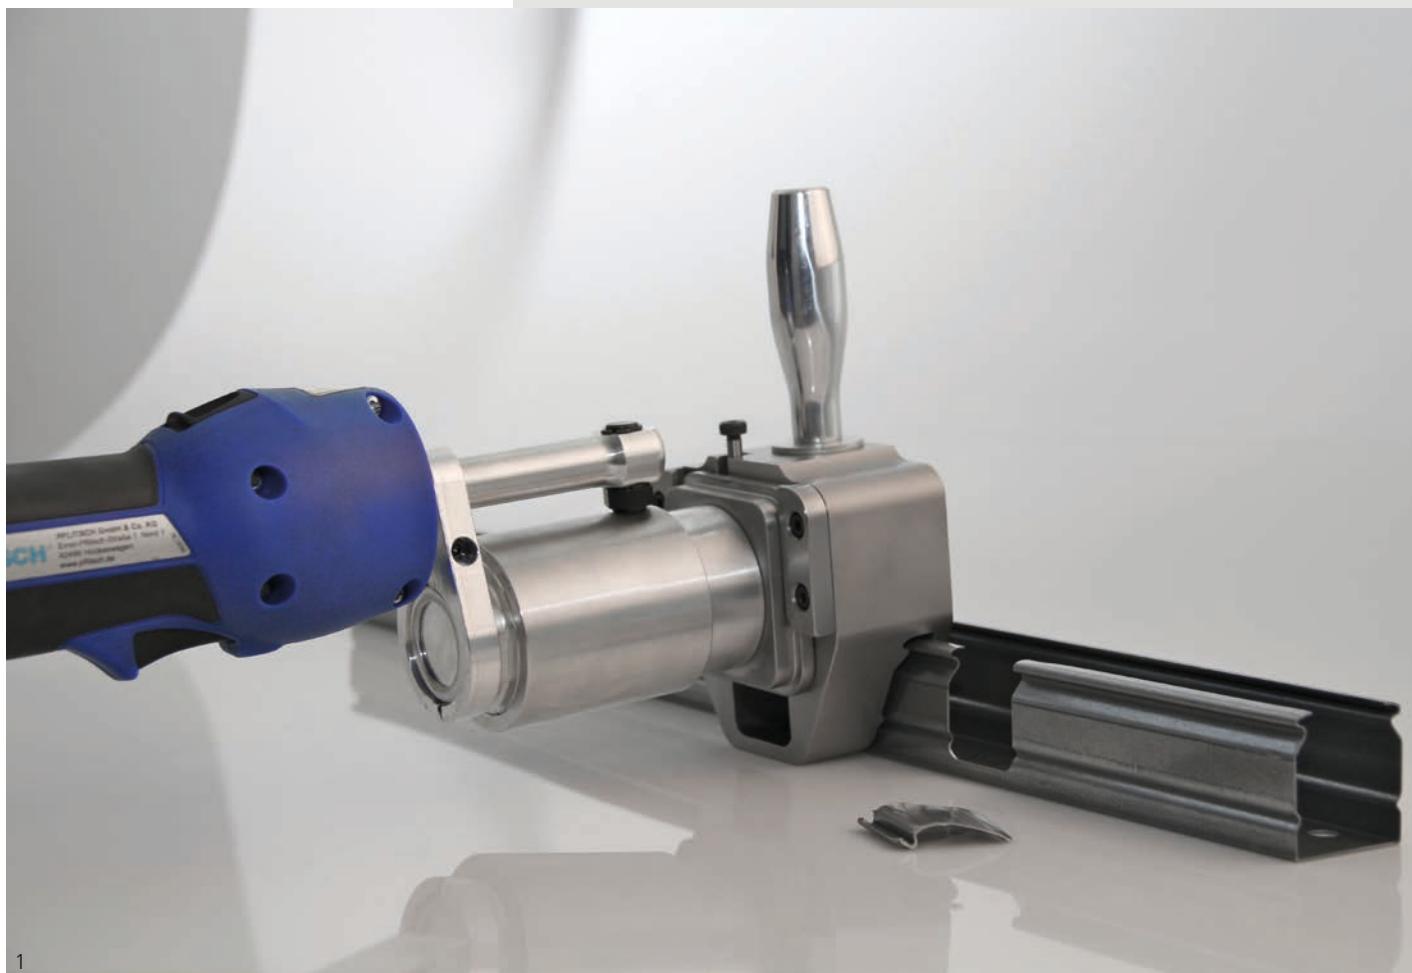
Ausklinkwerkzeug für PIK-Kanäle
